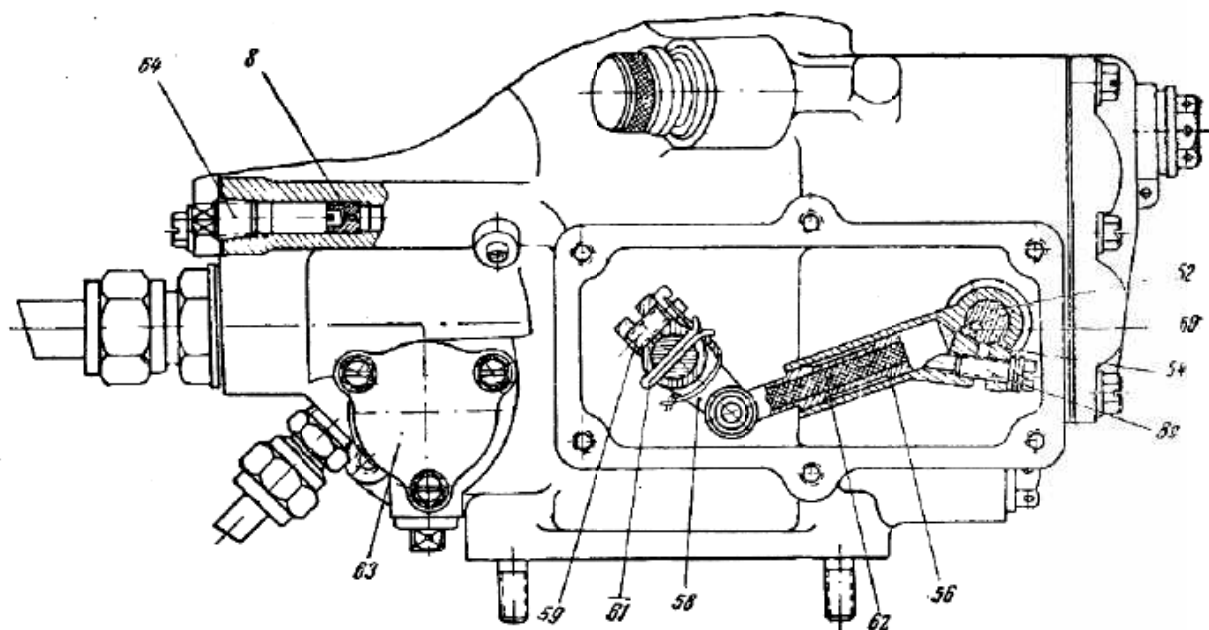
Вузол кулісного механізму: 8 – відсмоктувальний жиклер; 52 – валик важеля дозувальної голки; 54 – куліса; 56 – повзун; 58 – важіль куліси; 59 – гвинт; 60 – шпонка; 61 – конічний штифт; 62 – фетр; 63 – кришка паливного клапана; 64 – пробка; 81 – гвинт
